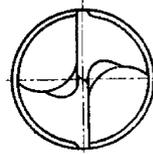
Richtig ge-spitzter Bohrer-kern.
